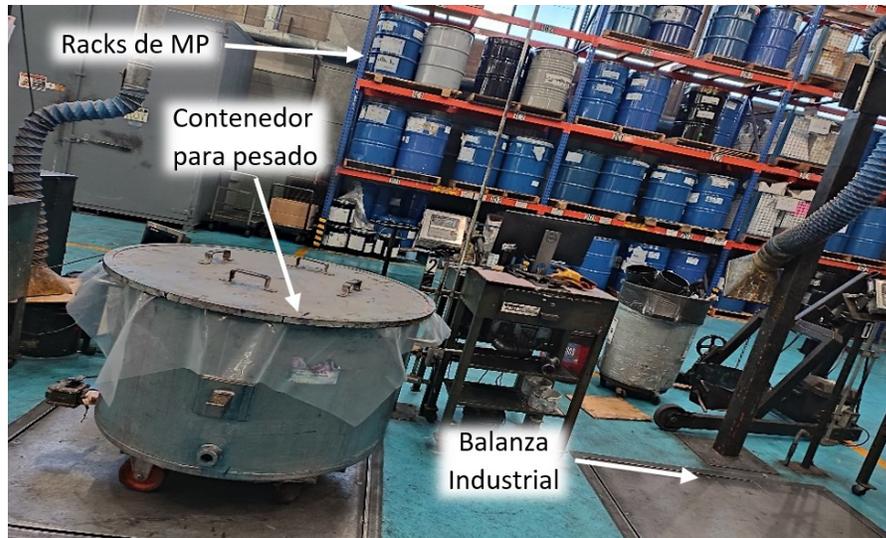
Área de pesado de la planta NW en Siegwerk México, 2022
